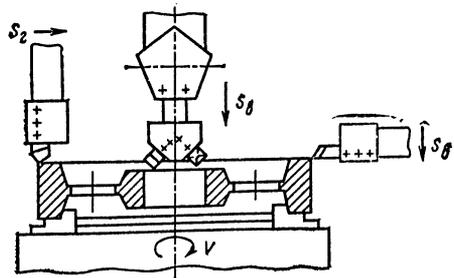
Схема обработки заготовки на токарно-карусельном станке
